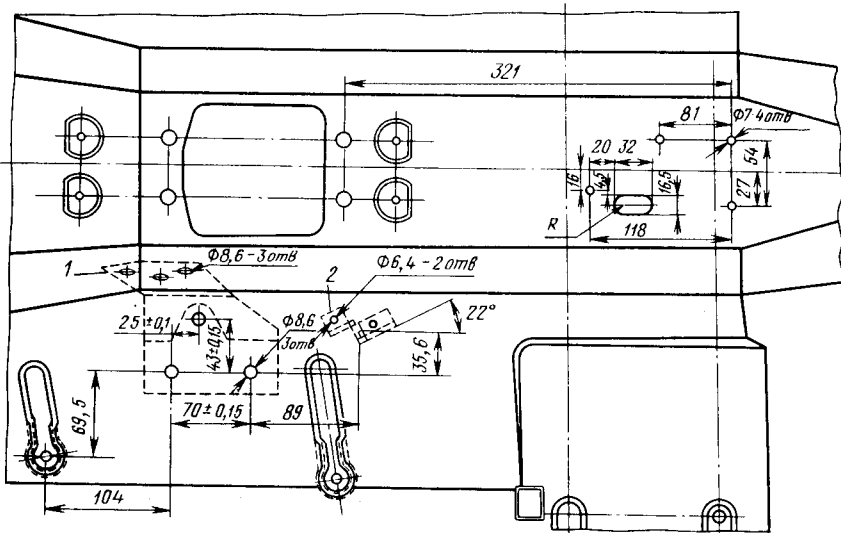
Расположение отверстий и места крепления кронштейнов для ручного привода тормозных механизмов на полу кузова (вид сверху из пассажирского салона): 1 — кронштейн промежуточного рычага; 2 — кронштейн крепления оболочки переднего троса. Справочный размер 745 мм дан от задней кромки окна для контроля уровня и заливки масла в коробку передач
